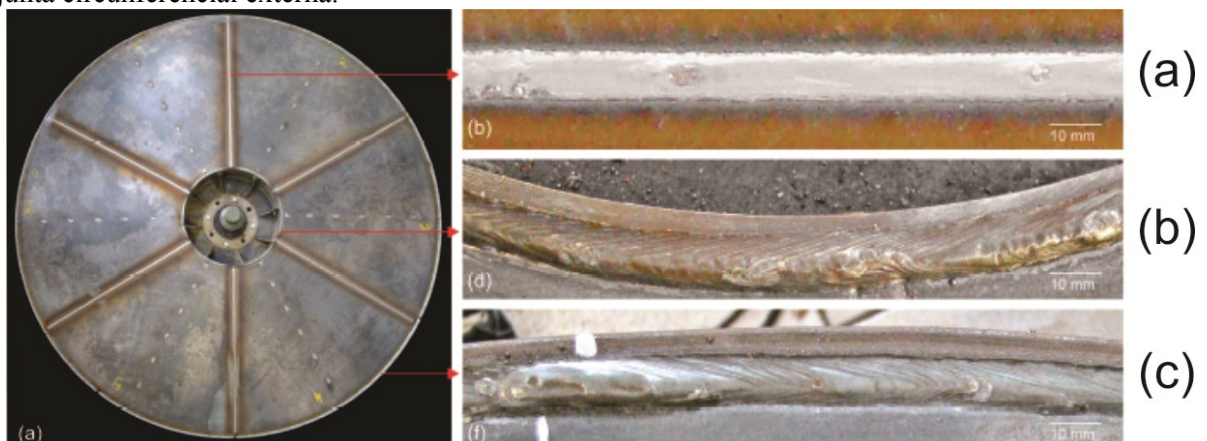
União dos componentes da roda de aço dos tratores pelo processo de soldagem MIG/MAG.
